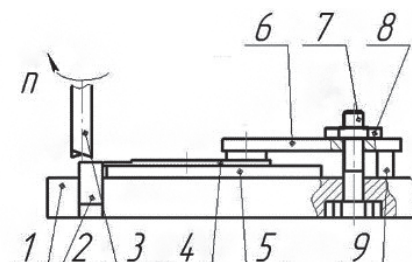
Технологическая схема обработки плоской дисковой заготовки фрезерованием: 1 — стол станка; 2 — координирующий штифт; 3 — фреза; 4 — плоская дисковая заготовка; 5 — опорная площадка; 6 — прижимная планка; 7 — болт; 8 — гайка; 9 — упор
